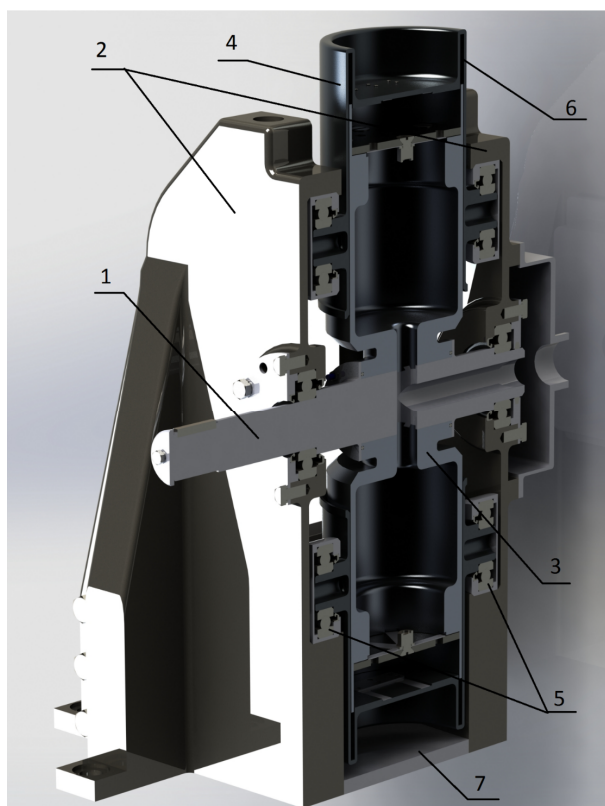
Компрессор ротативный безмасляный двухцилиндровый
